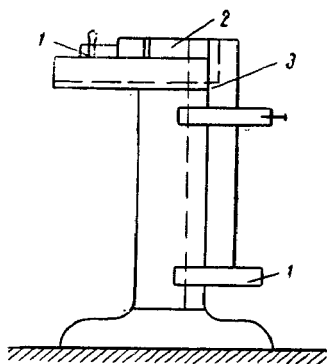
Приспособление для вставки петушков в шлицы коллекторных пластин:
